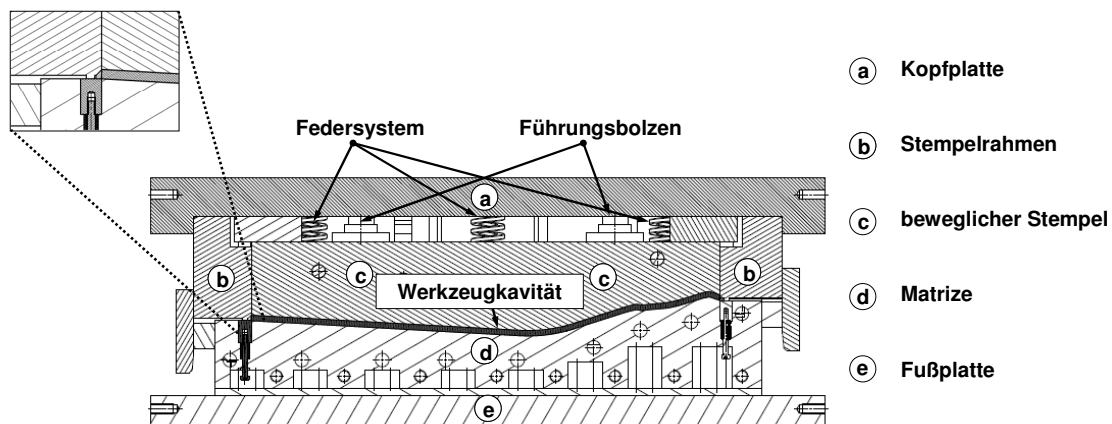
Schematischer Werkzeugaufbau mit kraftgesteuertem Werkzeugschließvorgang
